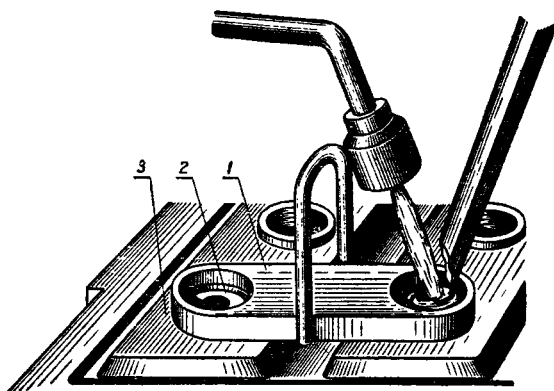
Сварка перемычки со штырем баретки:
